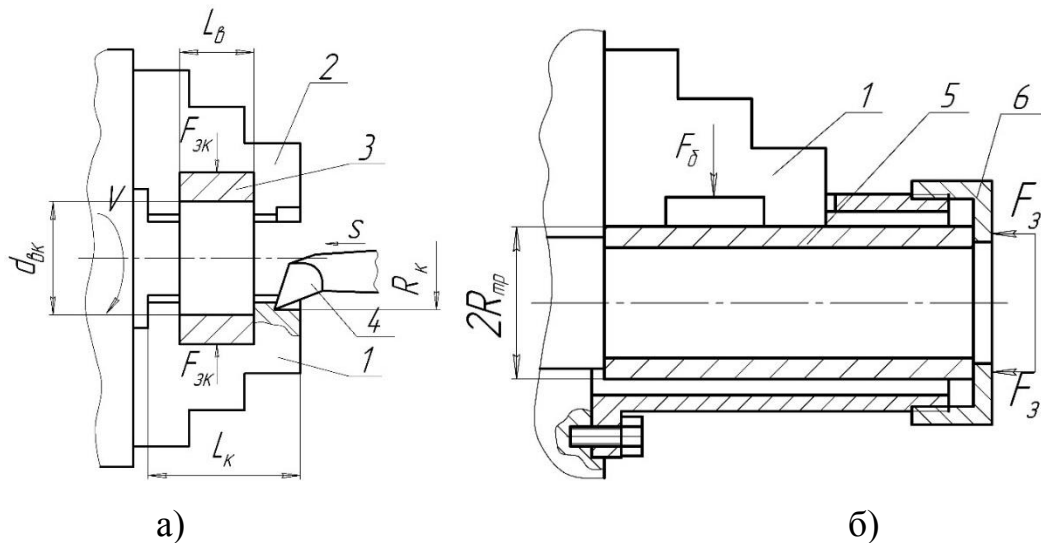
Схеми розточування кулачків а) і закріплення заготовки в патроні б): 1,2 – кулачки; 3 – товстостінна втулка; 4 – розточувальний різець; 5 – оброблювана заготовка; 6 – затискна гайка.
